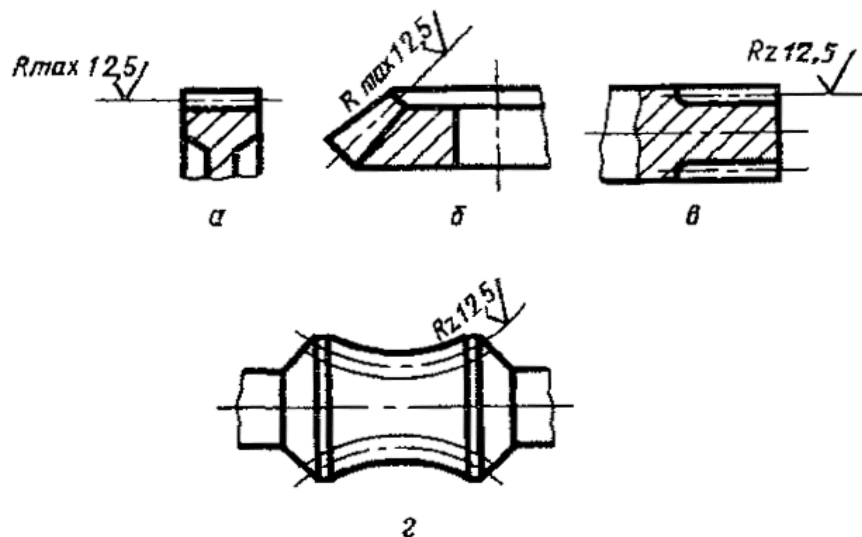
Обозначение шероховатости рабочих поверхностей зубьев
